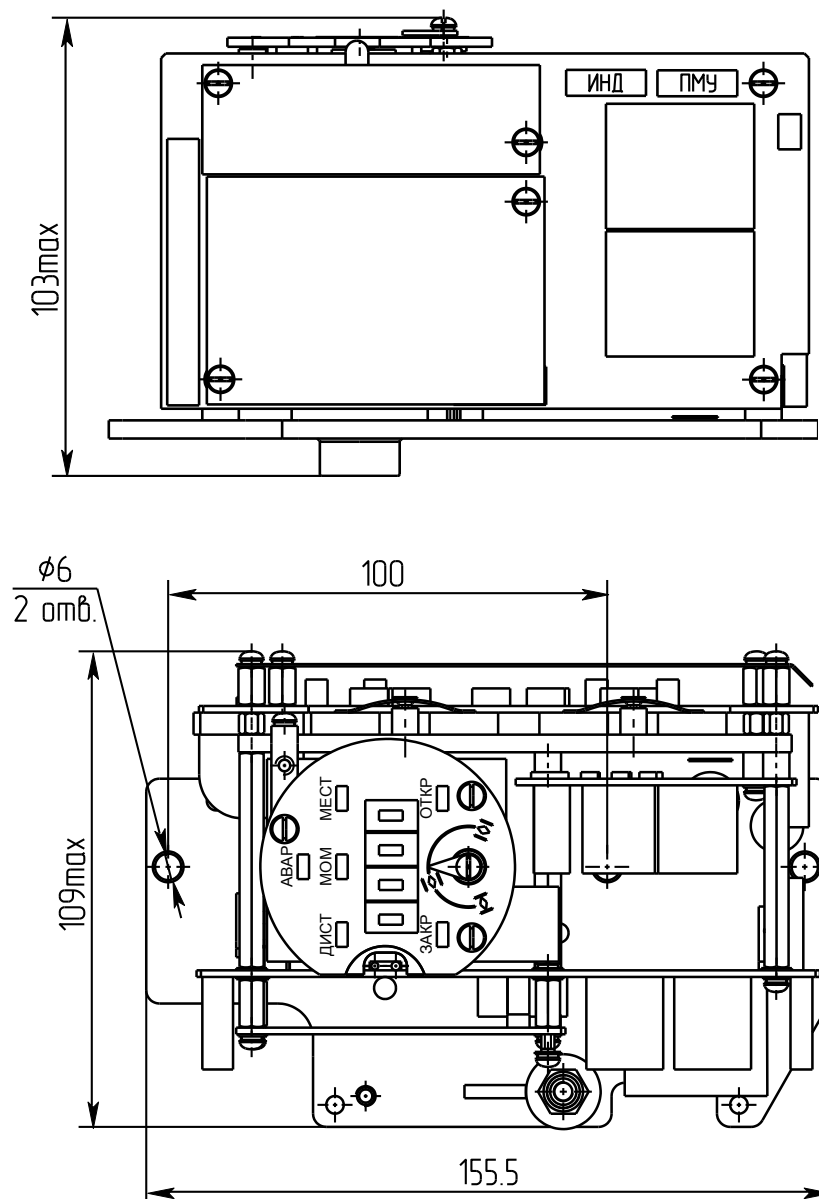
Контроллер КИМ1-2 для механизмов МЭО(Ф)-250, 630, 4000, 10000 и привода ПЭМ-В
